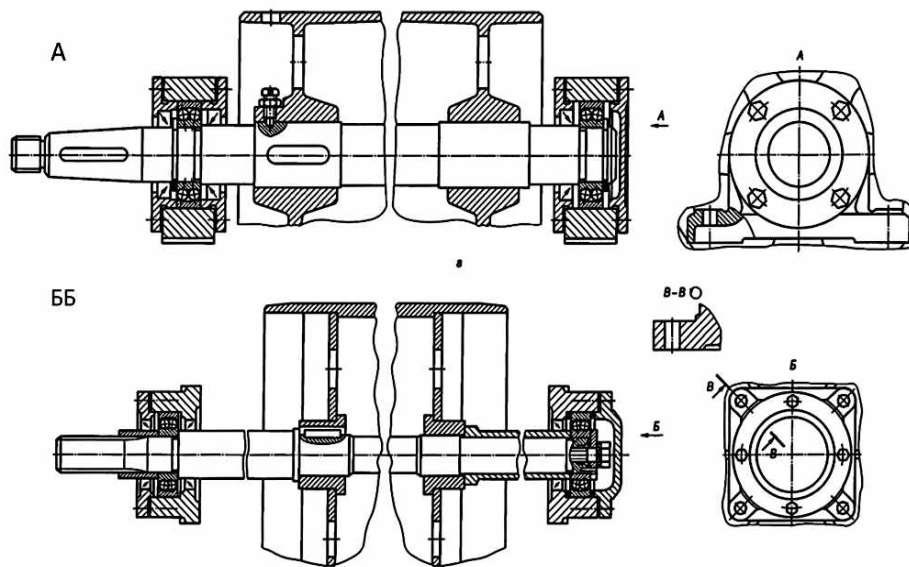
Барабани приводні на валу: А – литий; Б - зварний
